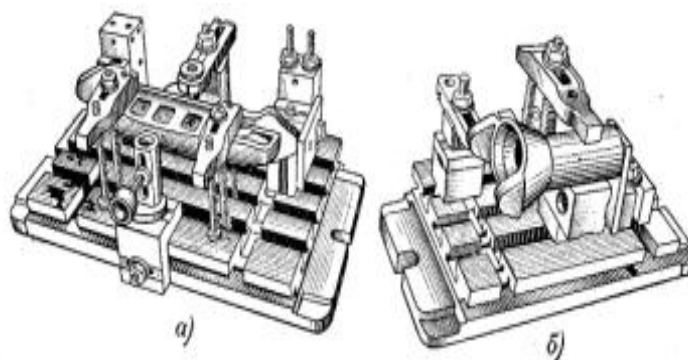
Приклади УЗП: а – для свердління, б – для фрезерування
